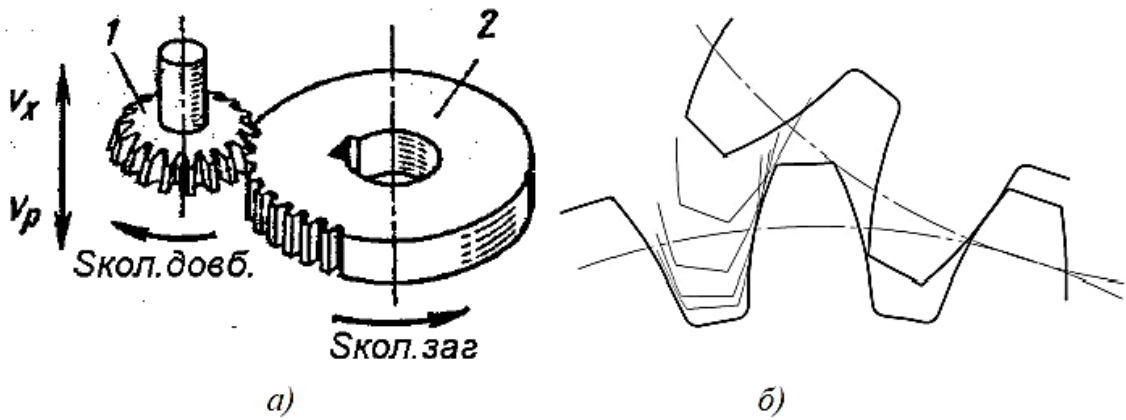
Схема формоутворення зубів циліндричного колеса: 1 – довбач; 2 – заготовка
